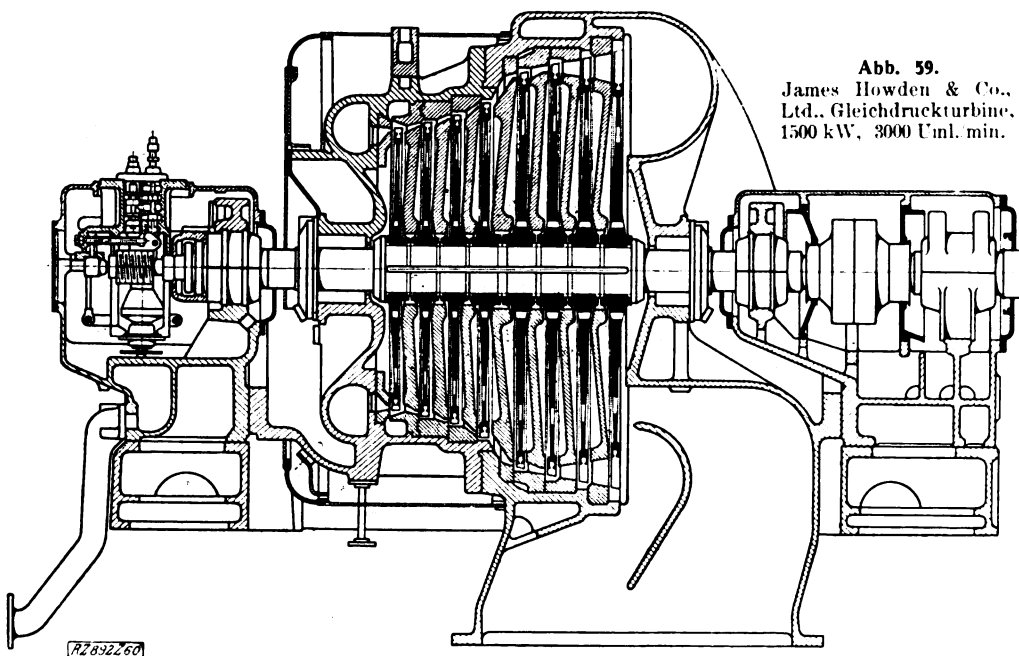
James Howden & Co., Ltd., Gleichdruckturbine, 1500 kW, 3000 Uml. min.
